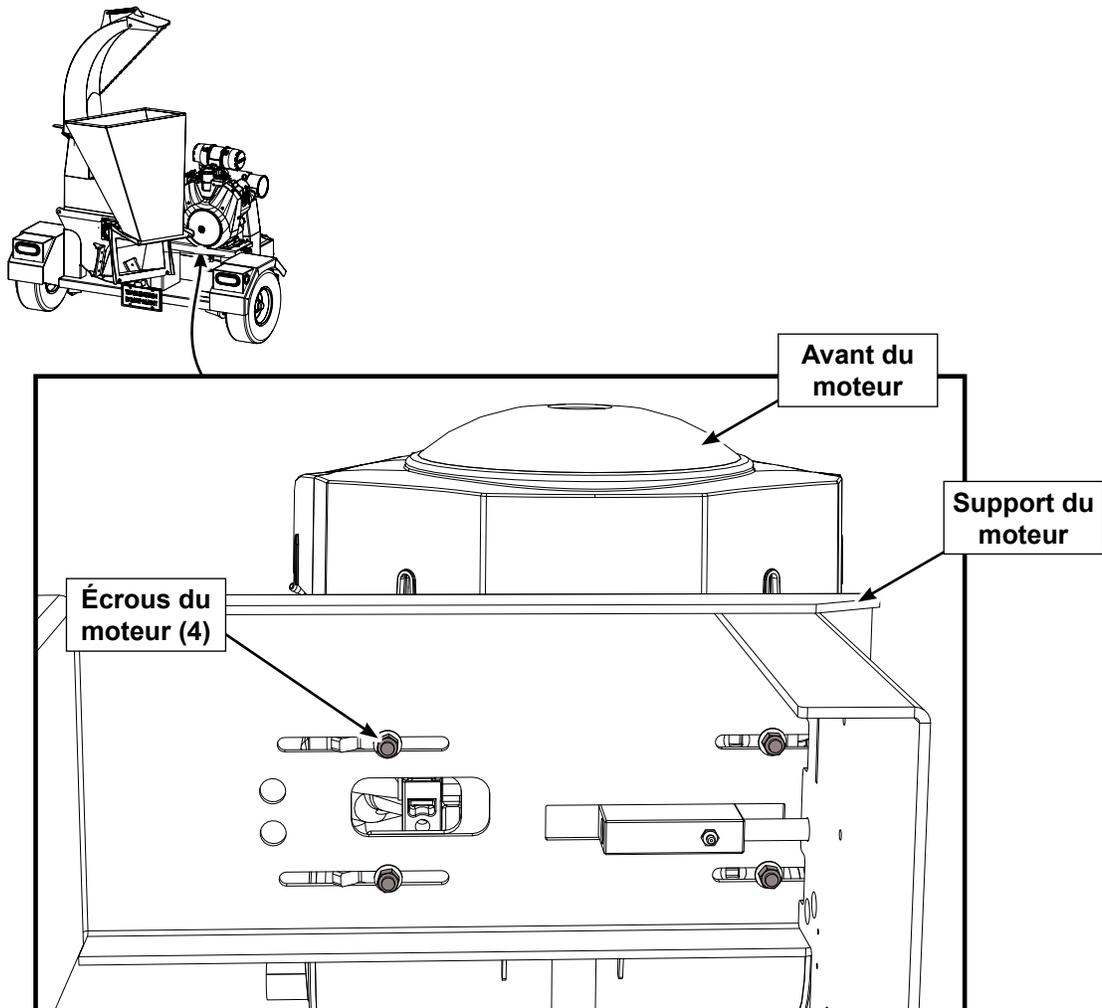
VUE DE DESSOUS DU SUPPORT DU MOTEUR
